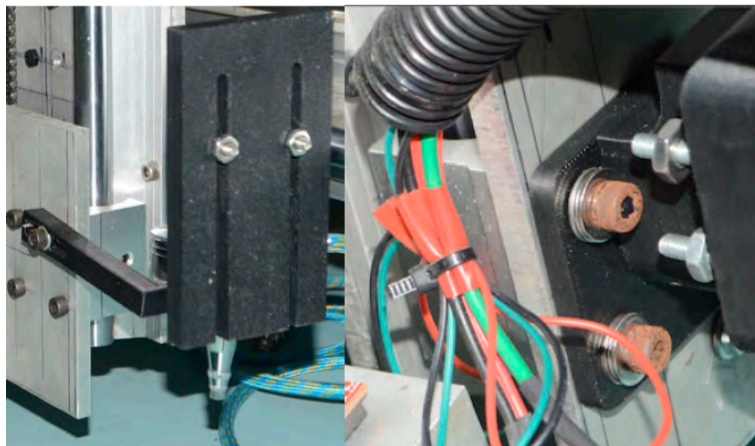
Herramientas ajenas al equipo CNC montadas sobre su estructura.
